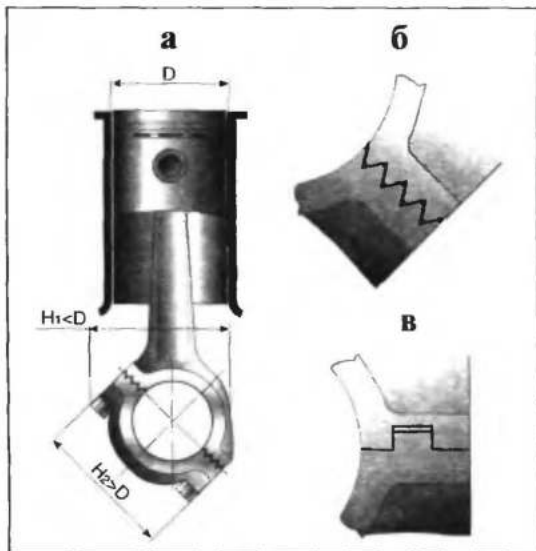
Косой стык крышки шатуна со стержнем: а — увеличенный диаметр шатунной шейки по сравнению с диаметром цилиндра — косой стык крышки позволяет собрать шатун, опустив его в цилиндр; б — треугольные шлицы; в — прямоугольные шлицы
